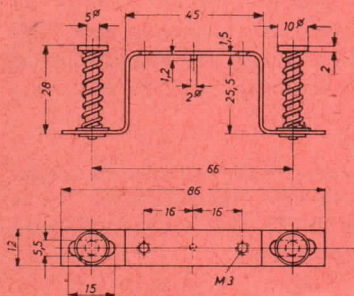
Federbrücke Typ Fb für die Thermoschalter in Normalausführung.
